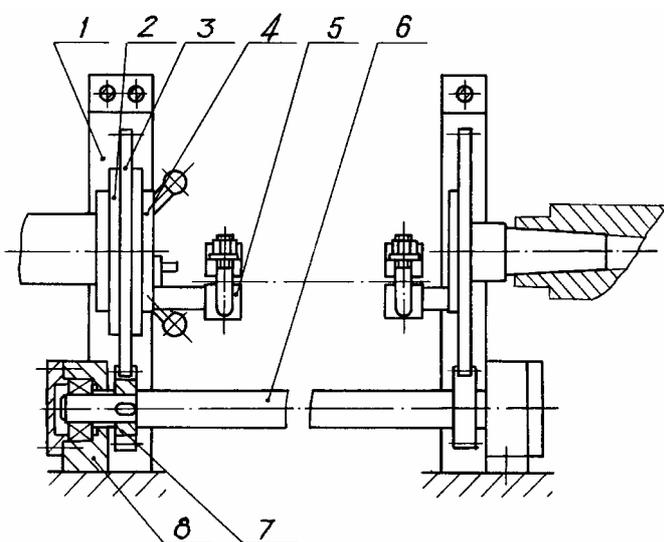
Схема вращателя коленчатого вала для напыления покрытий на его шейки: 1 – кожух; 2 – планшайба; 3 – колесо зубчатое; 4 – диск; 5 – клемма; 6 – вал; 7 – шестерня; 8 – корпус подшипника
